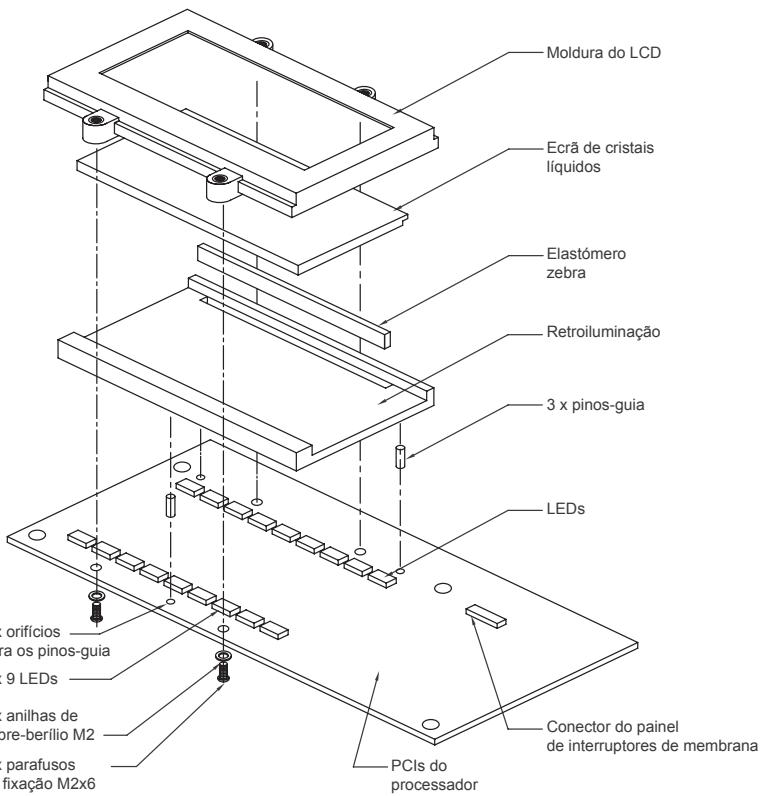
Gravura detalhada da montagem do Processador PCB V3
